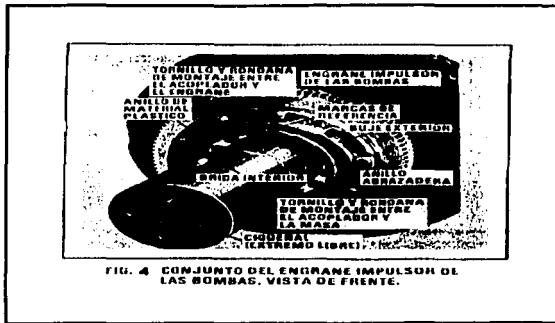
CONJUNTO DEL ENGRANE IMPULSOR DE LAS BOMBAS. VISTA DE FRENTE.
